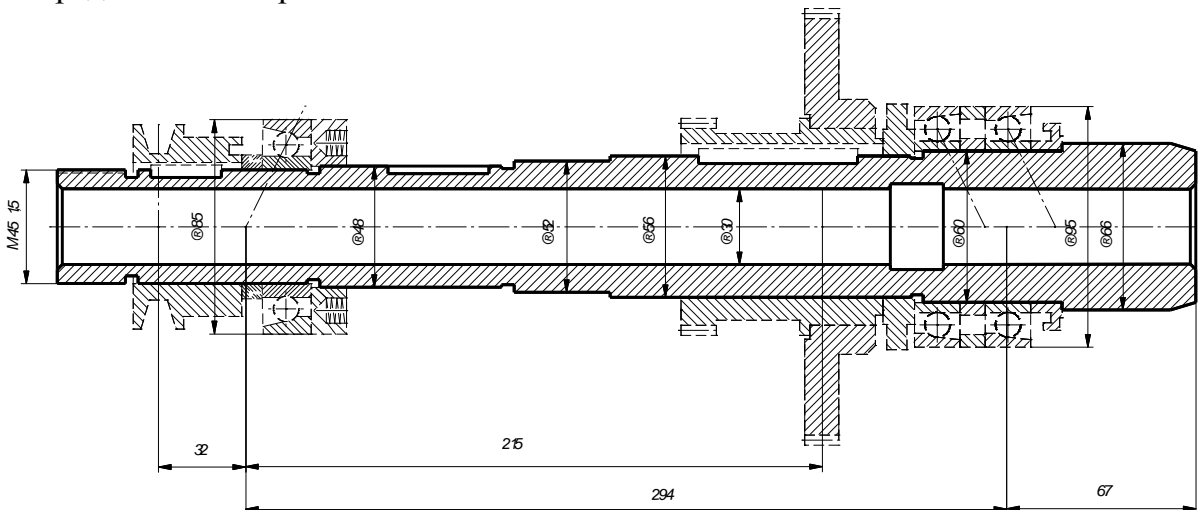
Конструктивна схема шпиндельного вузла верстата MC03
